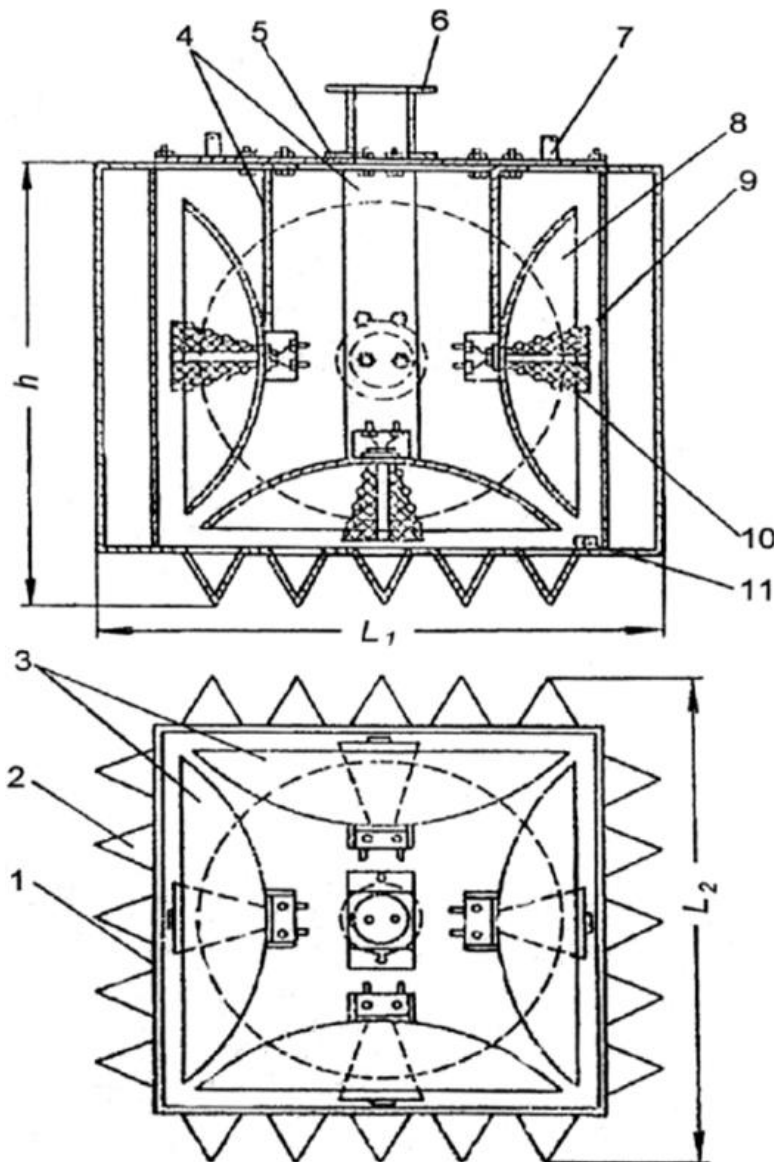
Установка для разогрева битума с использованием инфракрасного излучателя
